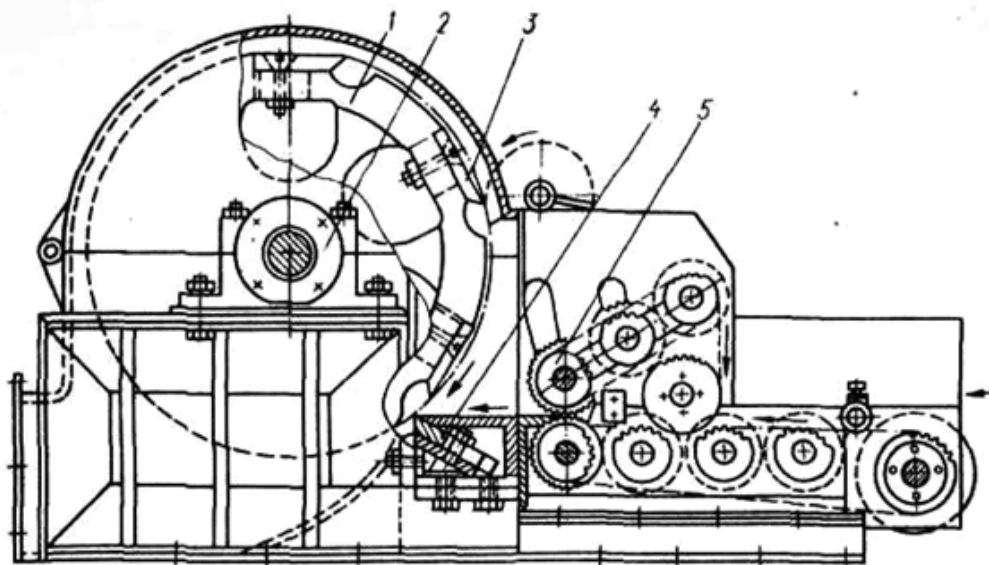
Схема барабанной рубительной машины с торцево - продольным резанием: 1 – ножевой барабан; 2 – откидной кожух; 3 – ножи; 4 – контрнож; 5 – вальцы для подачи древесины
